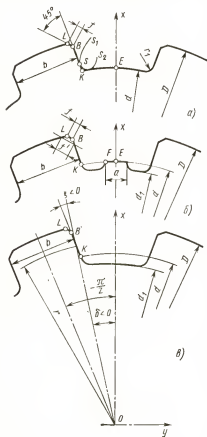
Профили шлицевых валиков с параллельными боковыми сторонами
